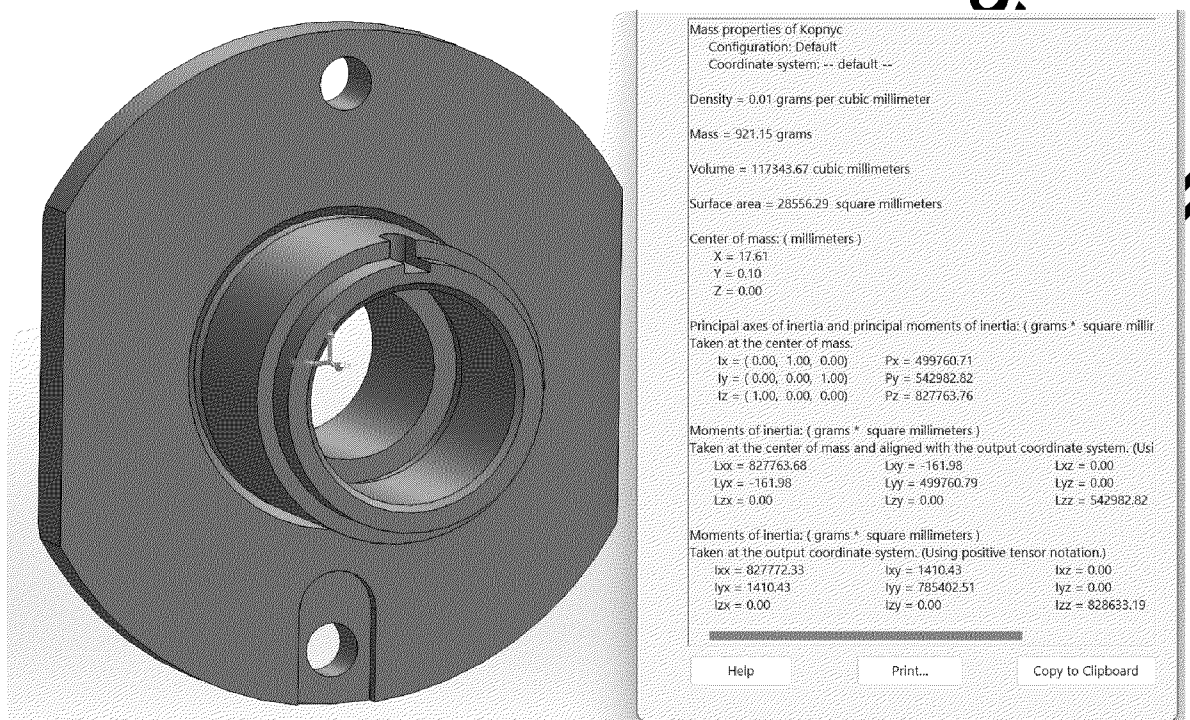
Тривимірна модель деталі «Корпус Д02120.1»
